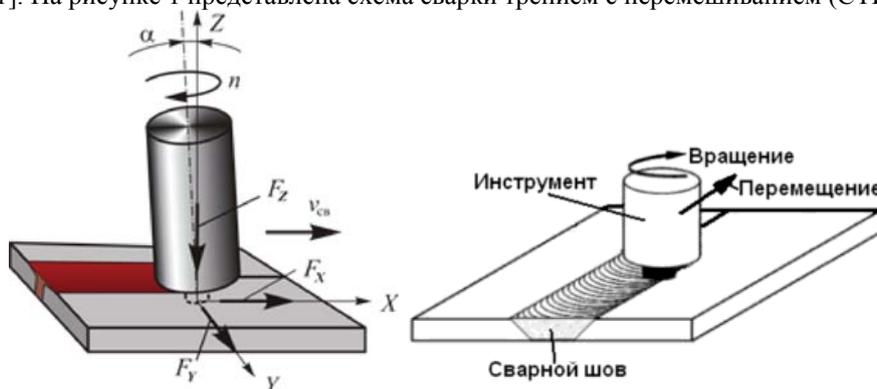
Схема процесса сварки трением с перемешиванием
